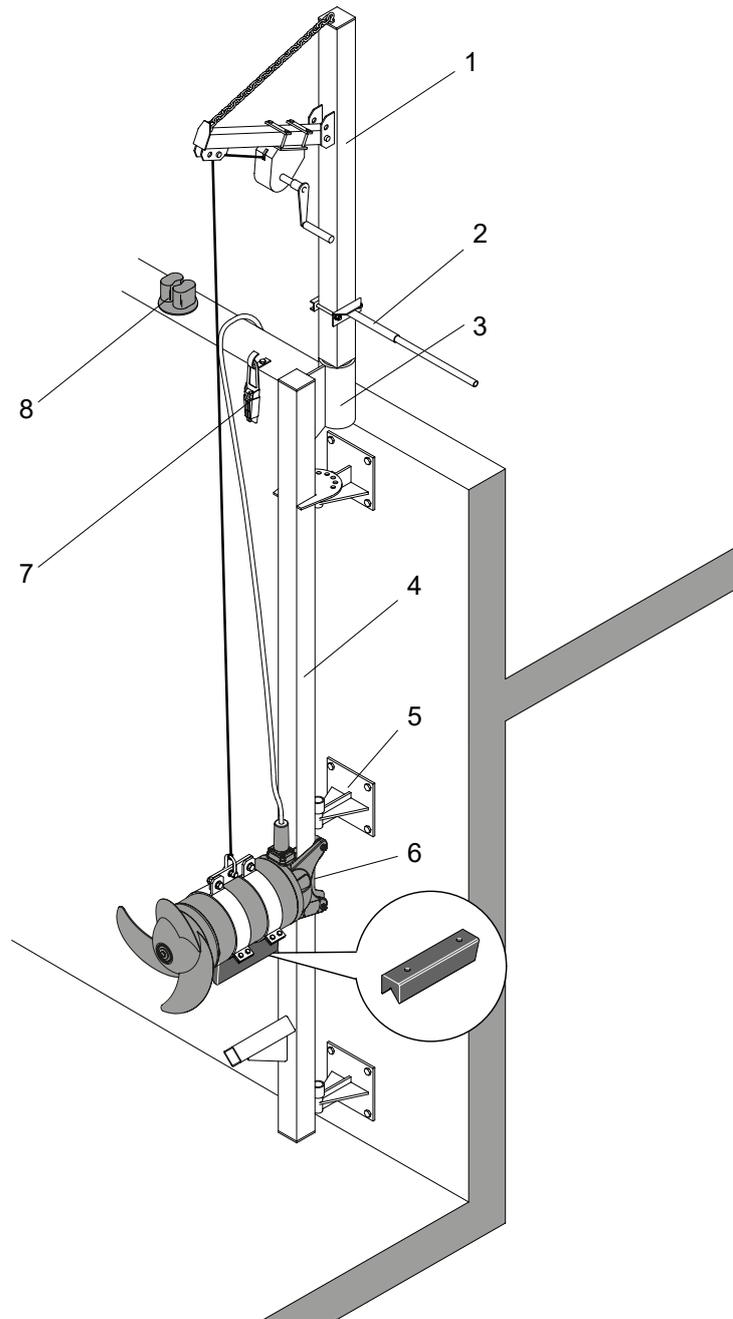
Exemple d'installation avec d'autres possibilités de fixation
